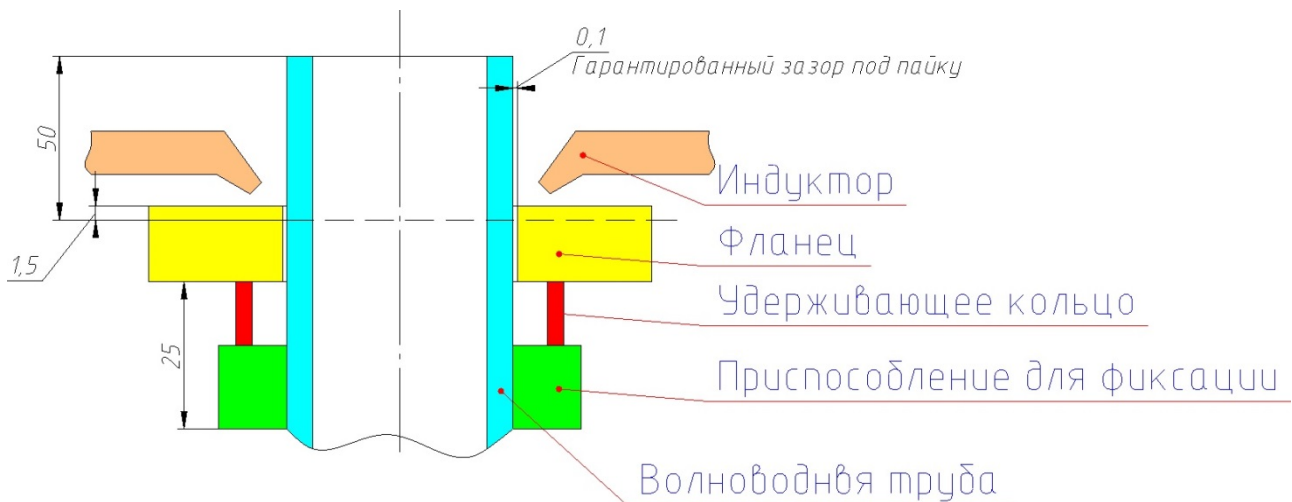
Схематический вид классической схемы сборки волновода под пайку
